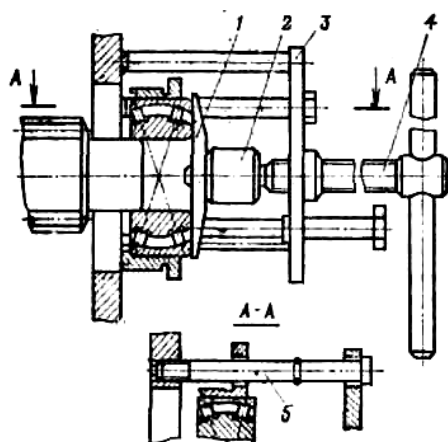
Пристосування для встановлення заднього підшипника проміжного вала И-801.31.000: 1 - шайба; 2 - наконечник; 3 - плита; 4 - гвинт; 5 – болт
